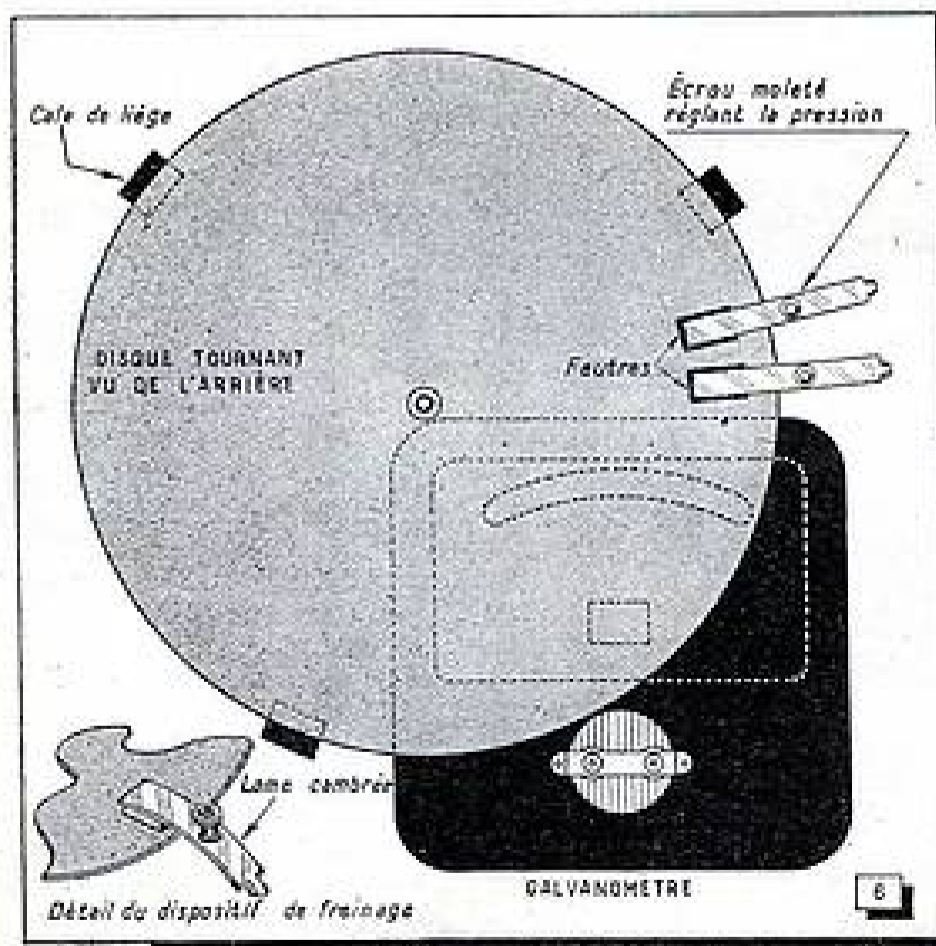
Des cales de liège maintiennent le disque à 1 mm environ en arrière du cadran.
